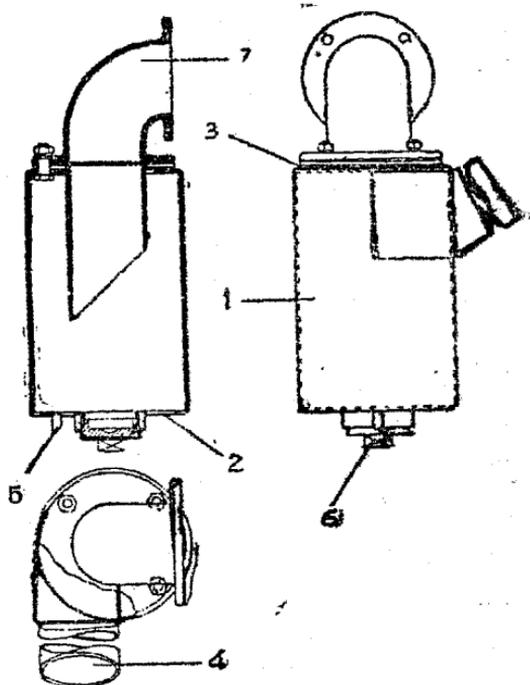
Отстойник в сборе: 1—корпус; 2—дно корпуса; 3—крышка корпуса; 4—патрубок подвода газа; 5—сливная трубка; 6—пробка люка; 7—патрубок отвода газа.
